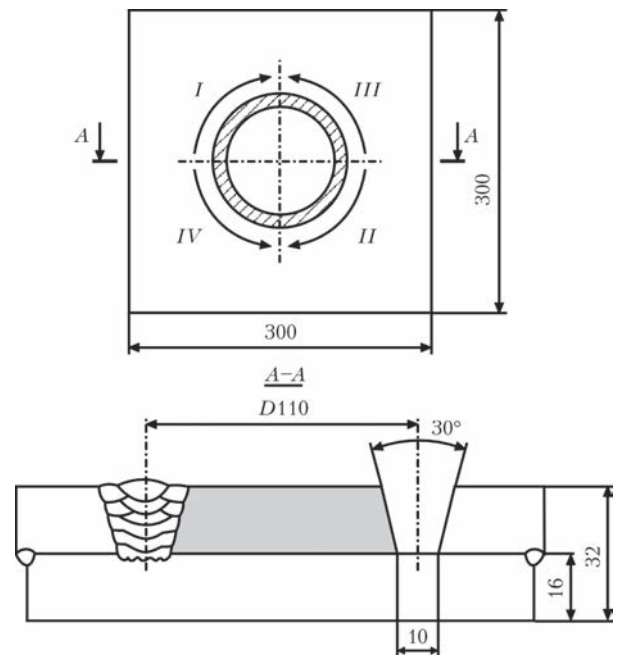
Схема технологической пробы «Marine» с порядком сварки налесточно-стыкового шва
